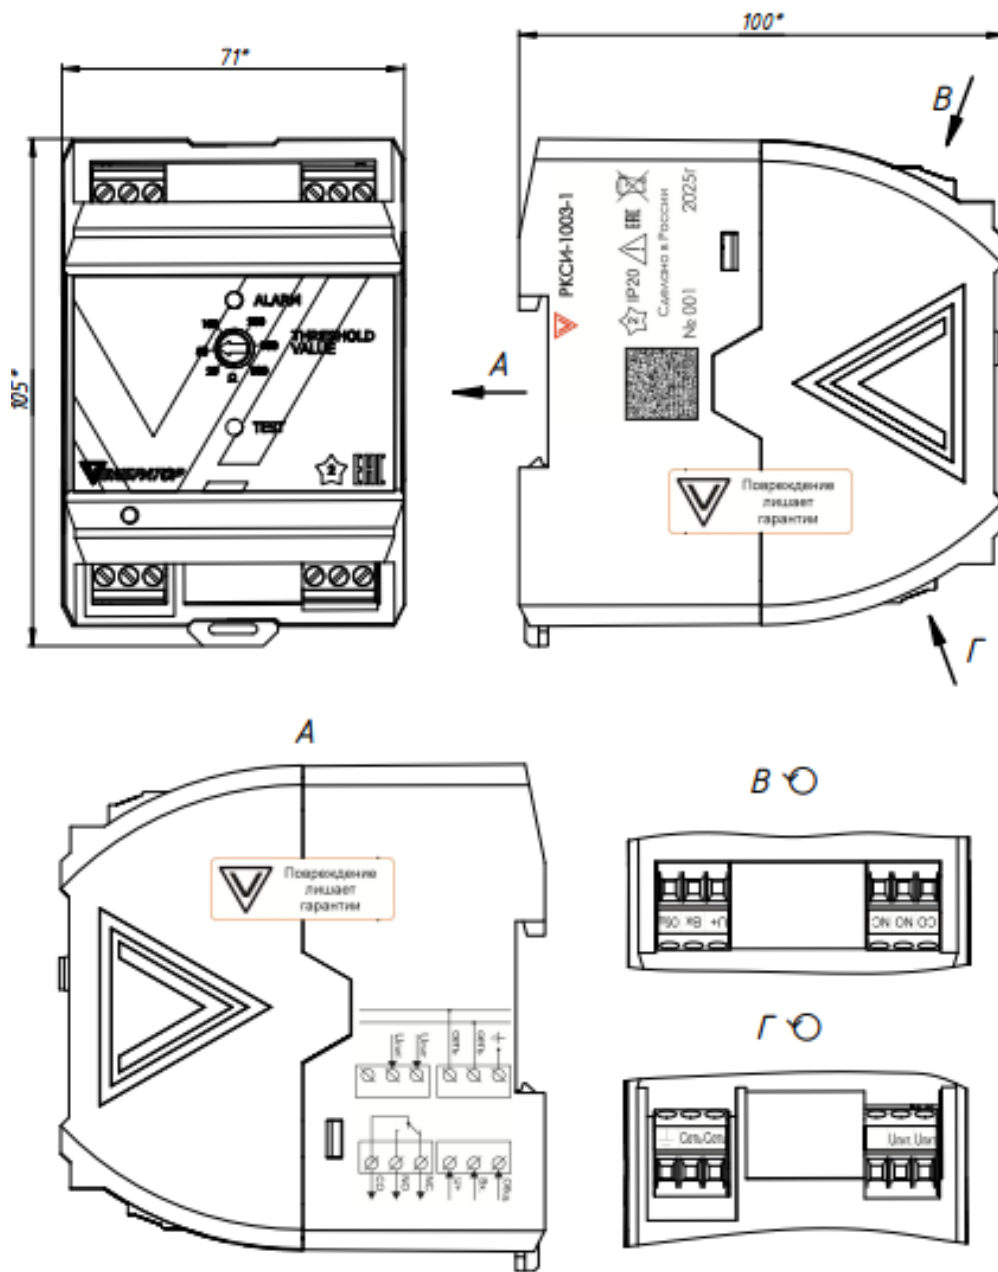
Внешний вид. Габаритный чертёж РКСИ-1003
